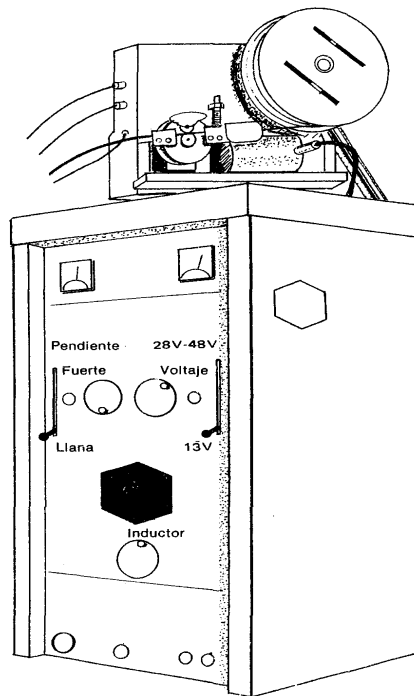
Fuente de poder de uso común para soldadura MIG
